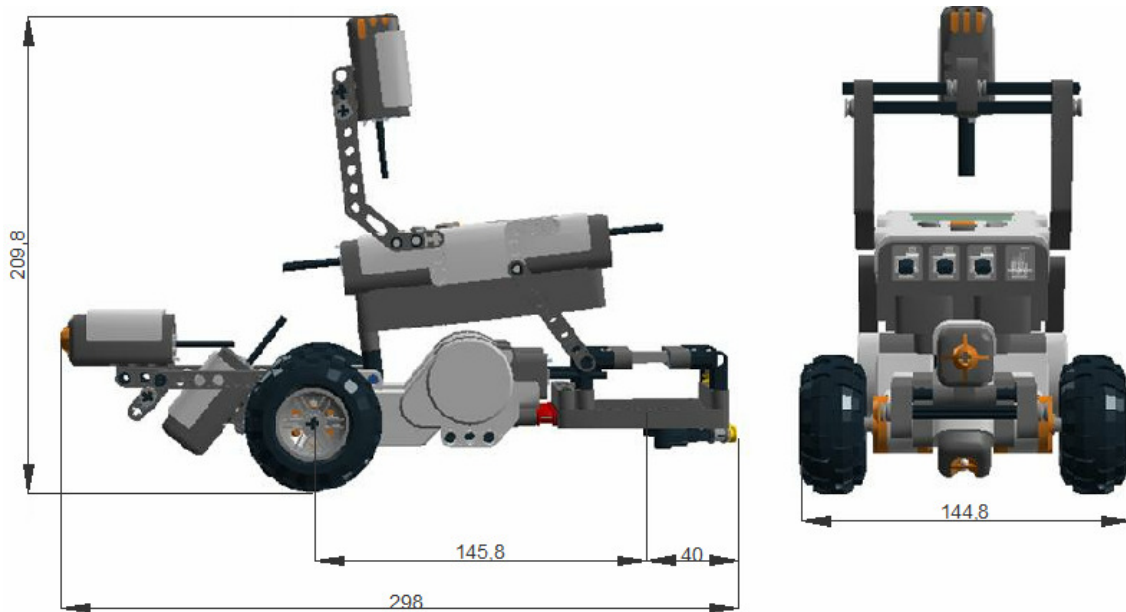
B.B3.): Dimensiones Segundo Montaje
